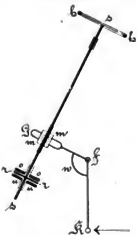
Erläuterung der Selbstspernung. Die Beschriftungen in dieser Figur sind dieselben wie in Figur 12.
